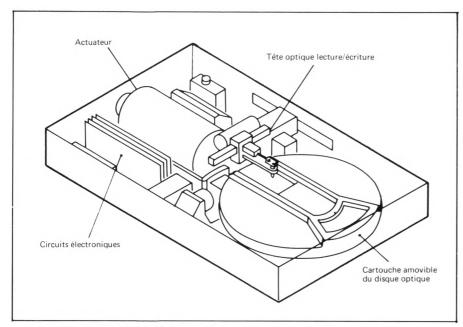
Vue de la mécanique d'une unité de disque optique numérique
